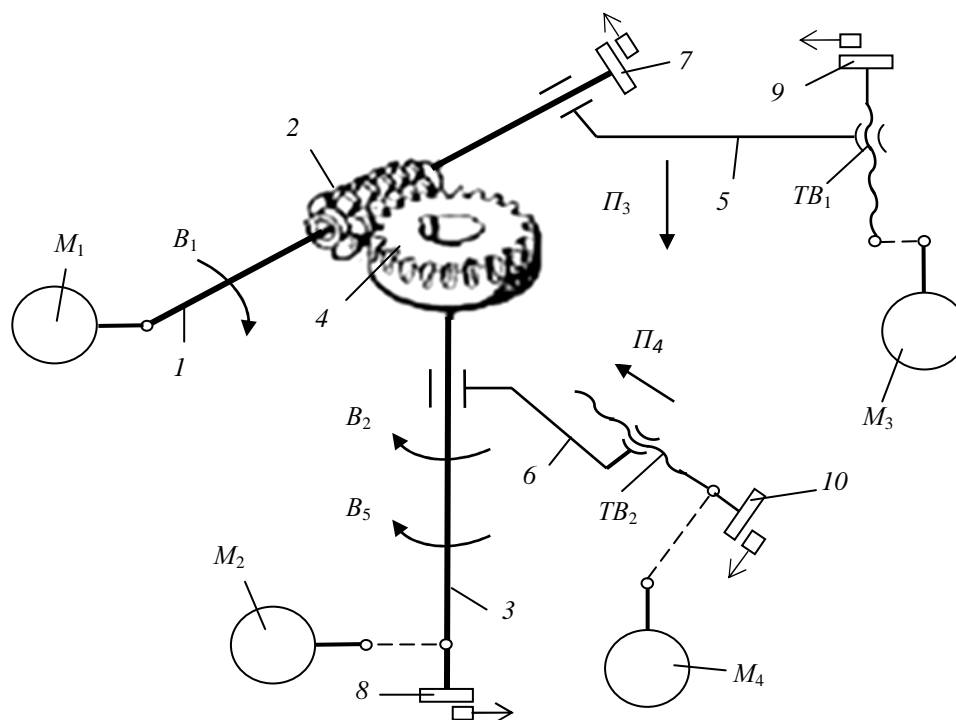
Структурная схема приводов зубофрезерного станка для обработки ЦЗК с наклонными зубьями
